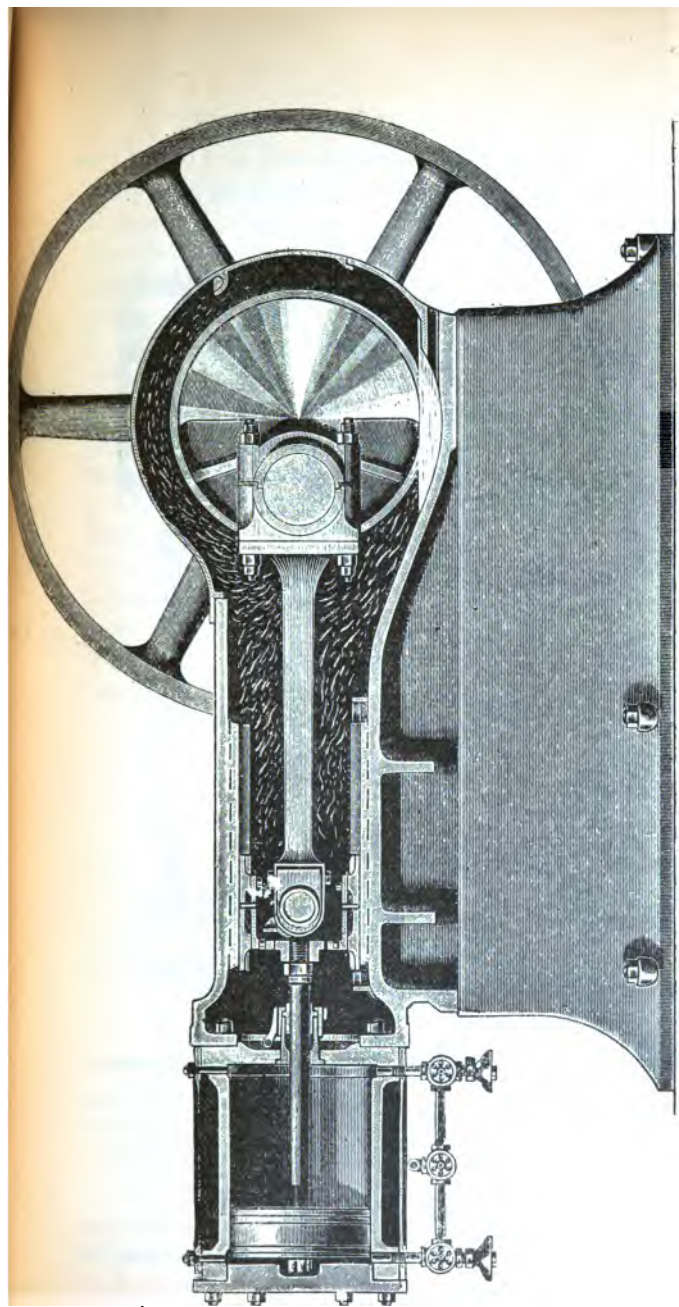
Machine américaine Ide. La puissance des diverses machines de ce type varie de 8 à 250 chevaux, et le nombre de tours par minute de 500 à 225. Montage du cylindre en *porte-à-faux*.
